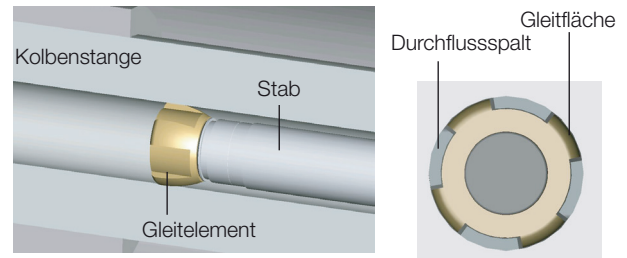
Detailsicht und Draufsicht Gleitelement
